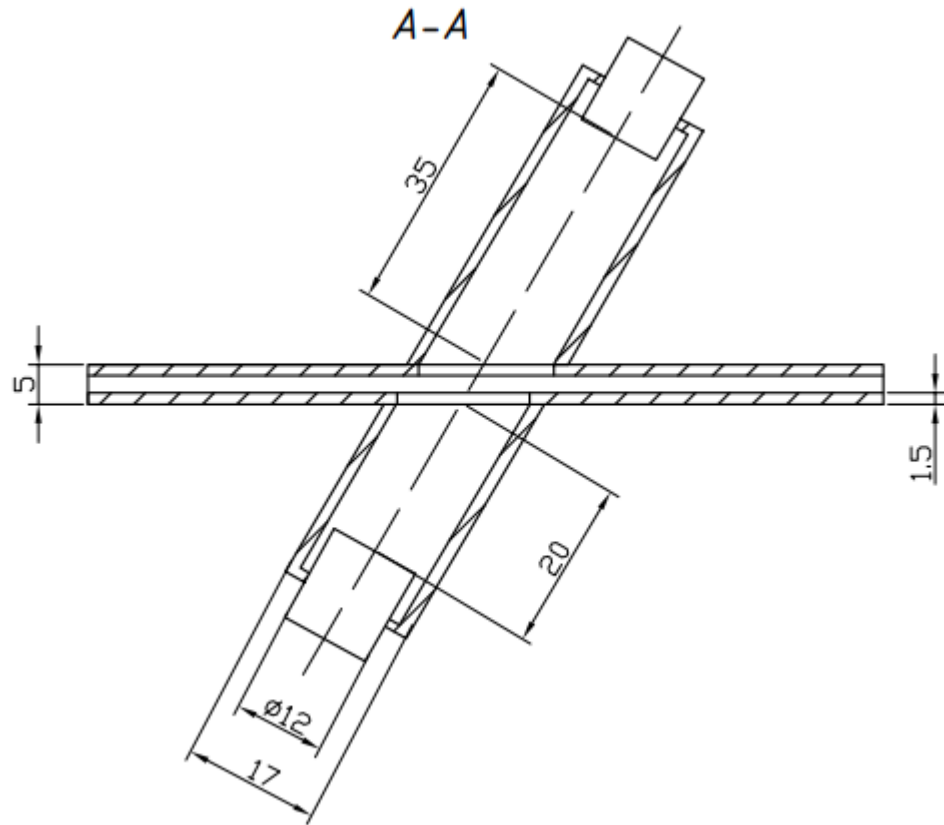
Конструкція сенсора вид в розрізі з боку
